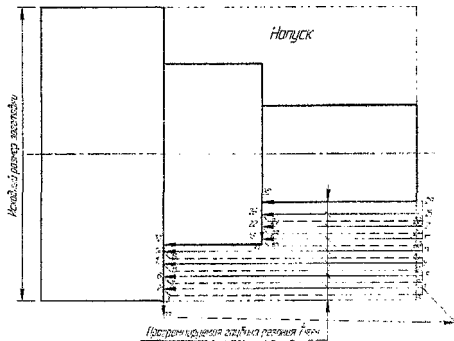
Схема удаления напуска и черного припуска из полукрытой зоны обработки
